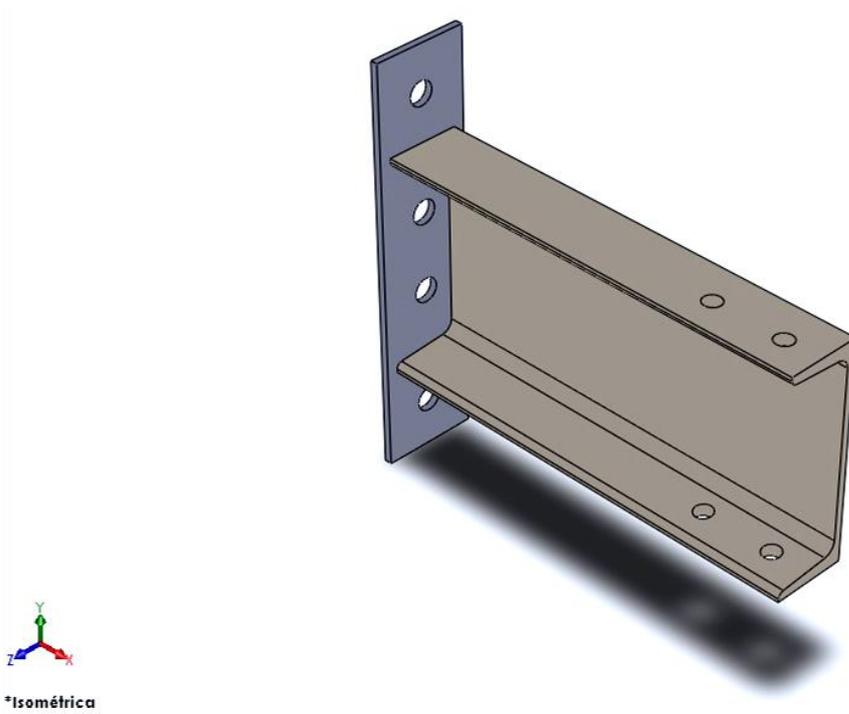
Modelo del soporte antivuelco tipo de las vigas carril.
